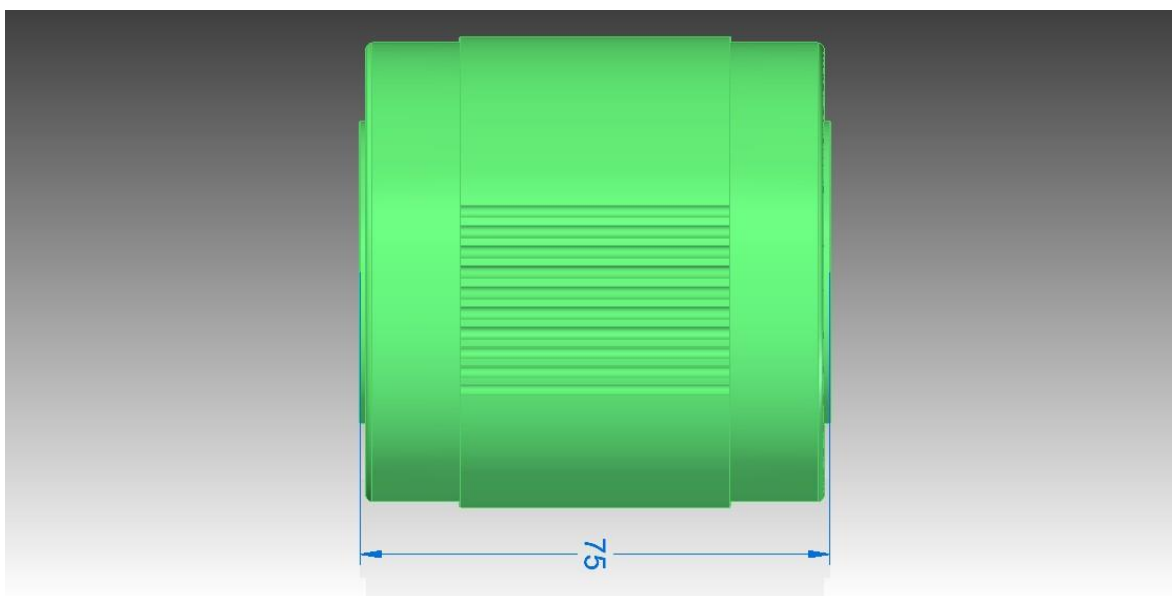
desenho técnico do *Chuck* (fonte: empresa).
